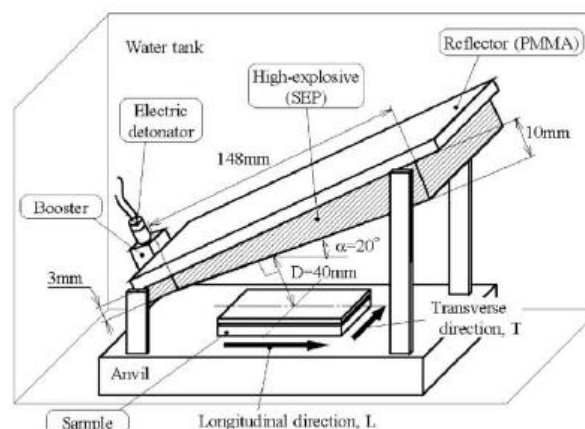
Técnica de soldadura por explosão debaixo de água (Hokamoto, et al., 2008).
